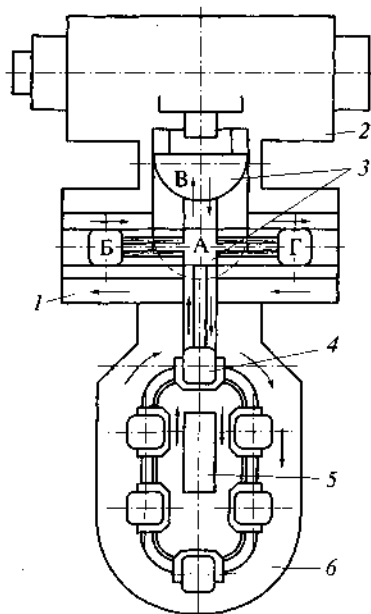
ГПМ на базе обрабатывающего центра:
